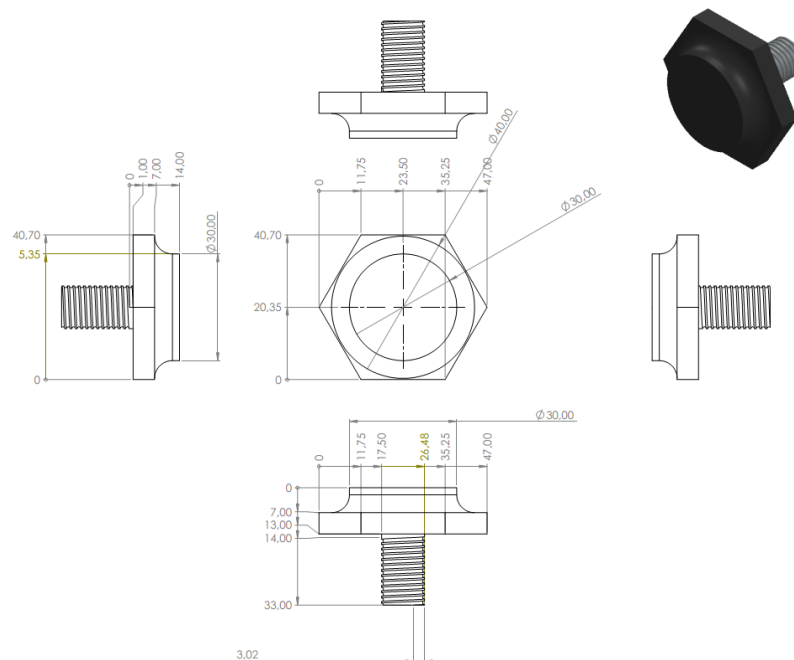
Mise en plan du pied sur SolidWorks.
